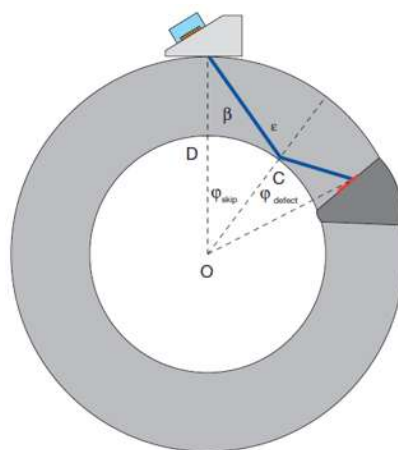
Examinación ultrasónica de una soldadura axial en una tubería [45].
